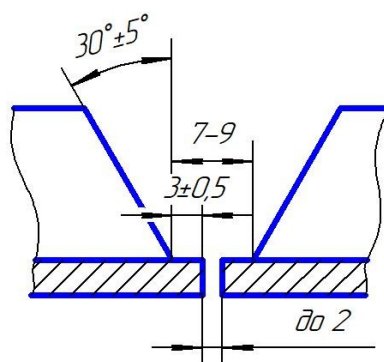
Схема разделки кромок двухслойных сталей под сварку с односторонним швом
